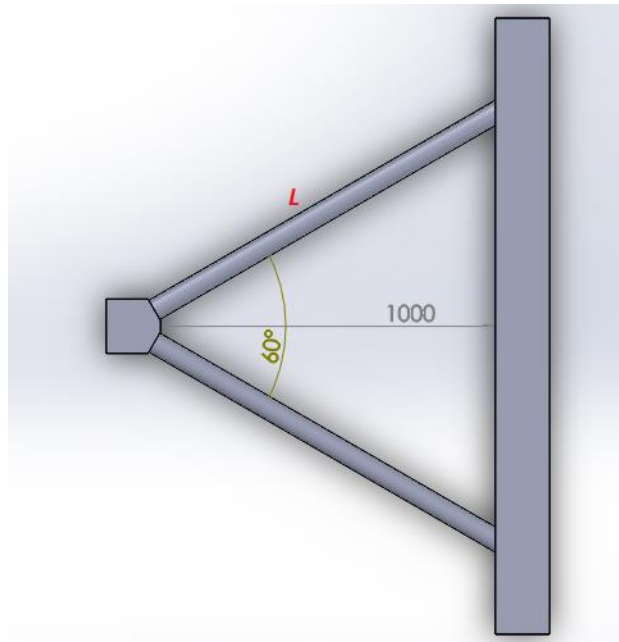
Vista en planta del sistema de despliegue; en el que se muestra la longitud del tubo
